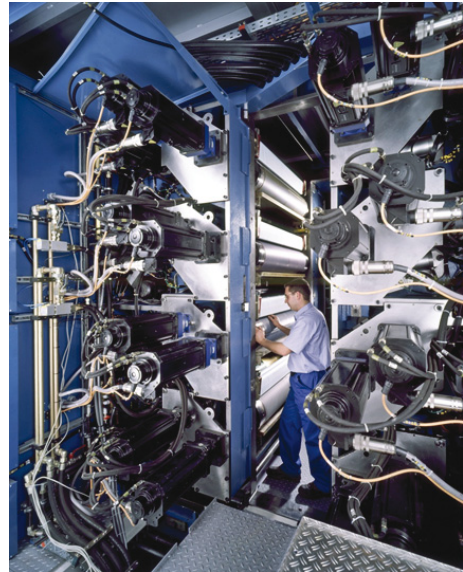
Druckmaschinen (© Koenig & Bauer AG)
